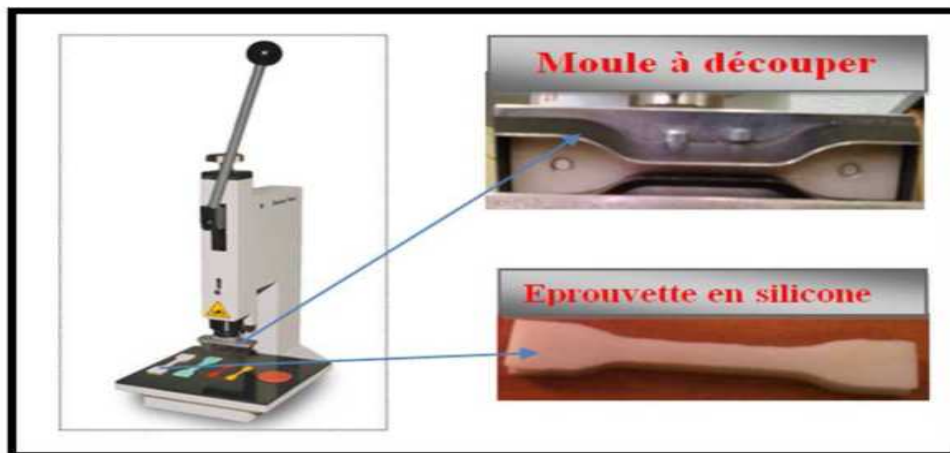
Presse manuelle Zwick 7101 coupe éprouvette.
